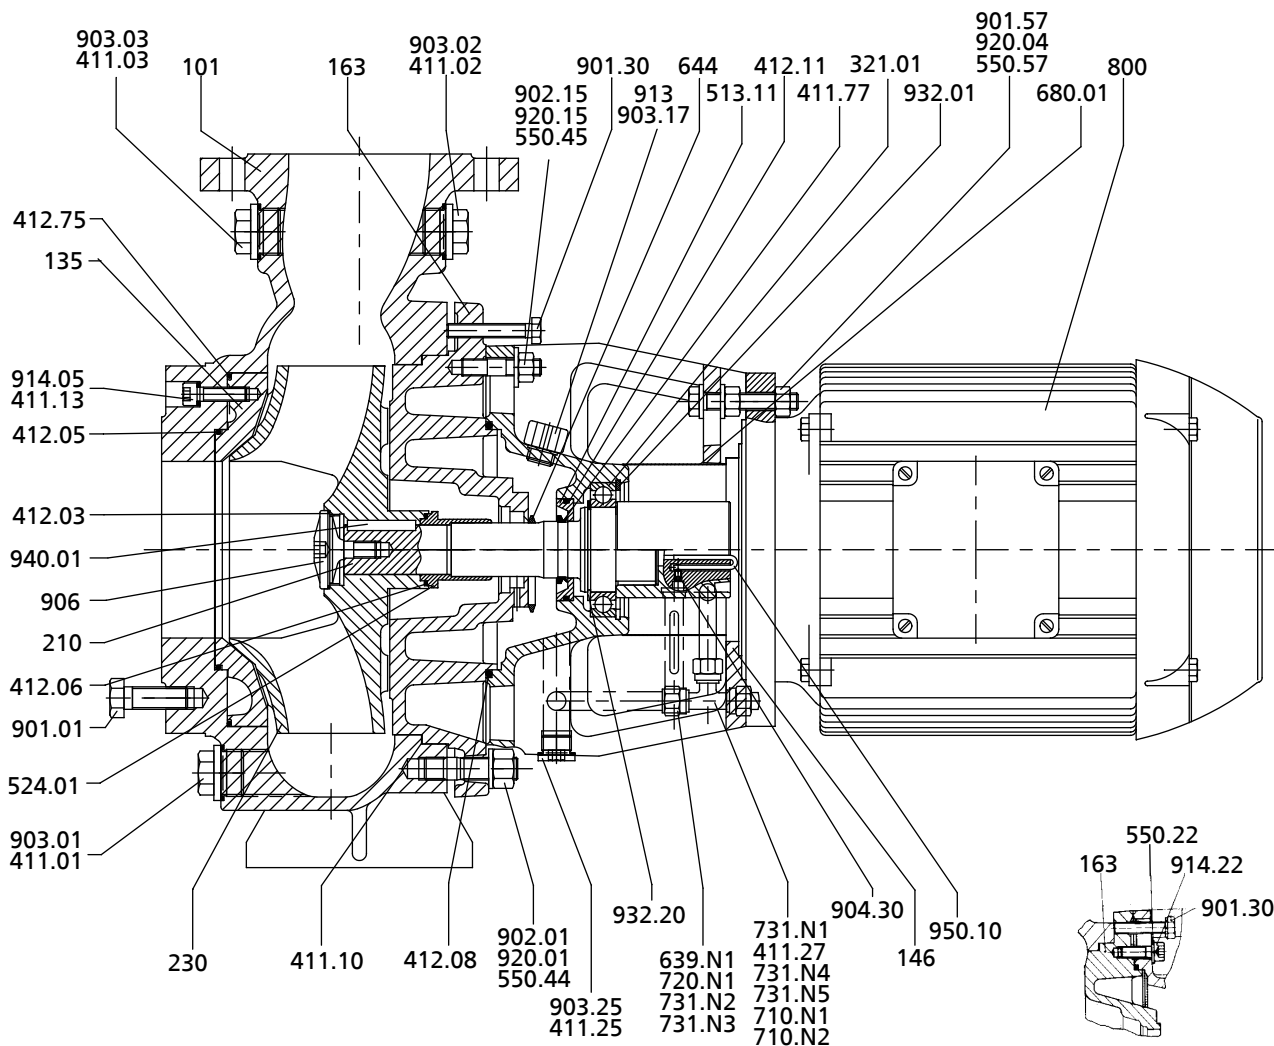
Сборочный чертеж исполнения GNNG, GDNG
